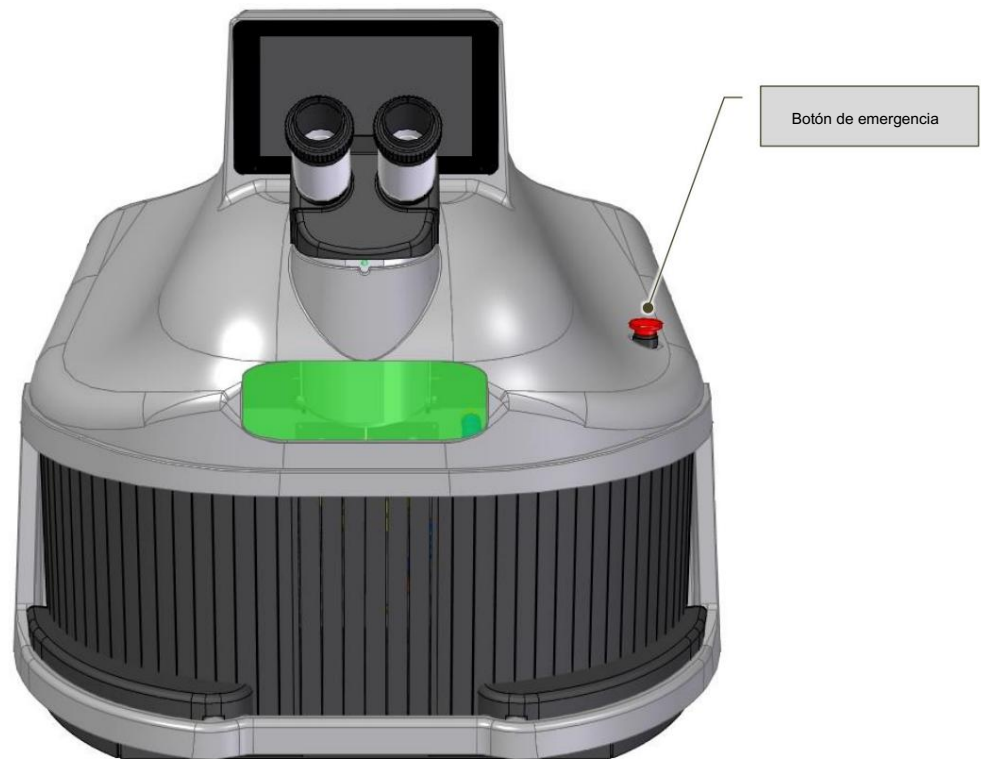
Botón de emergencia (vista interna de la cámara de soldadura)
